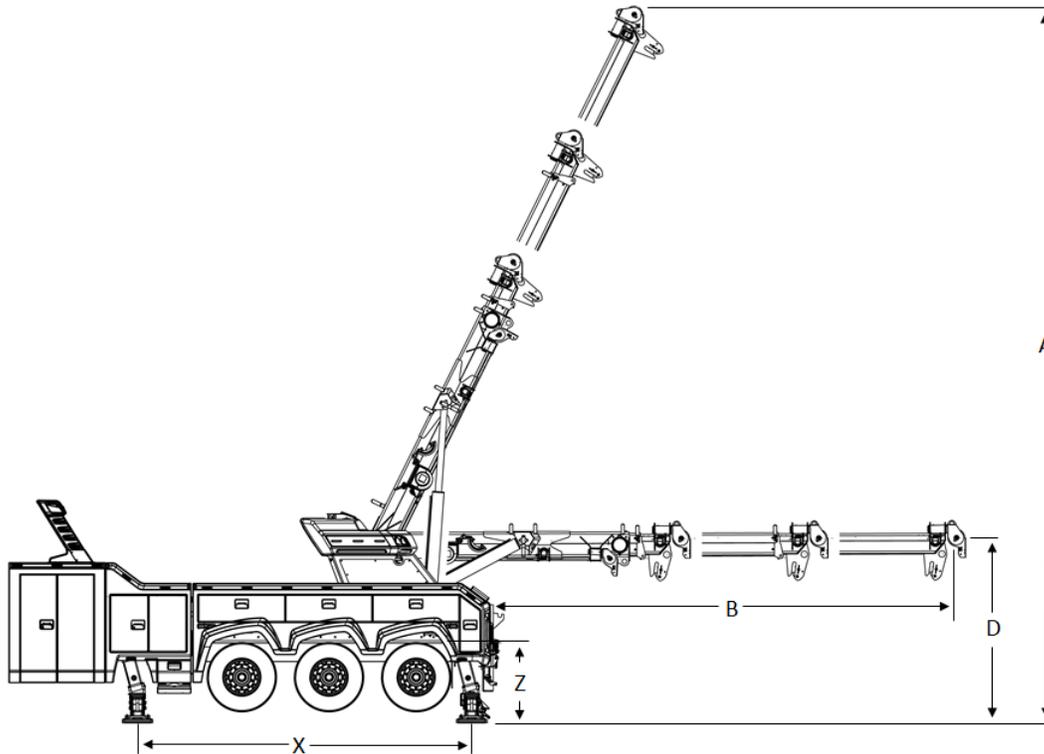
DIMENSIONS DE LA FLÈCHE ET DES STABILISATEURS - VUE LATÉRALE (EXEMPLE)
